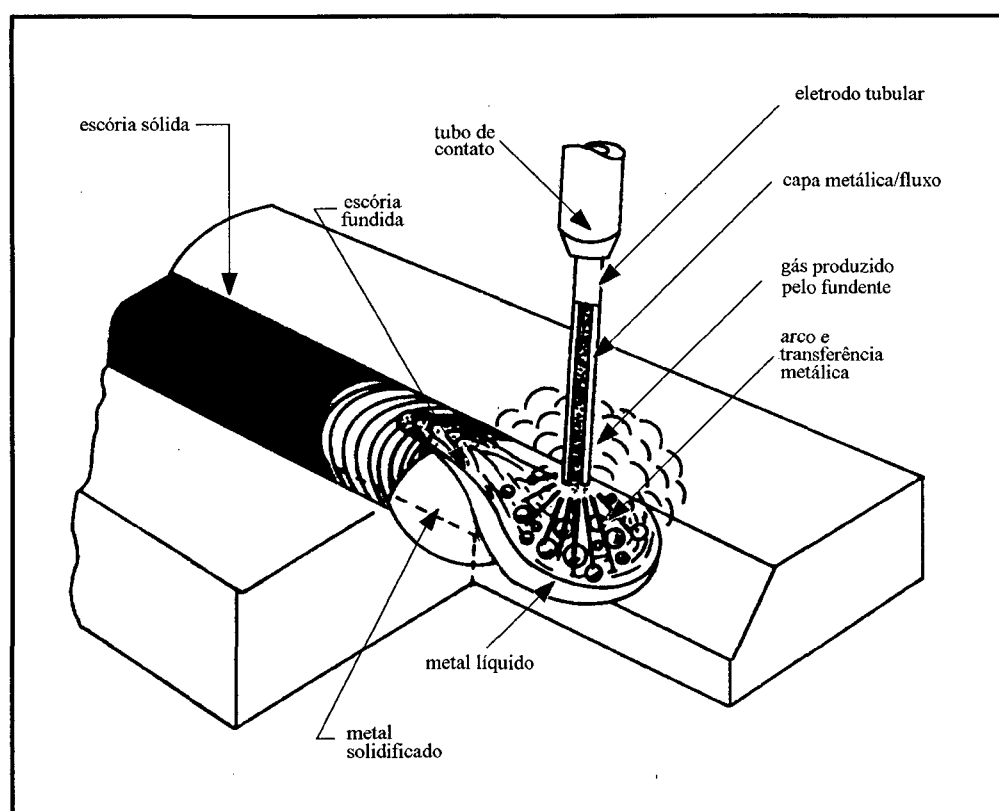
Esquema da soldagem com arame tubular autoprottegido [03].
